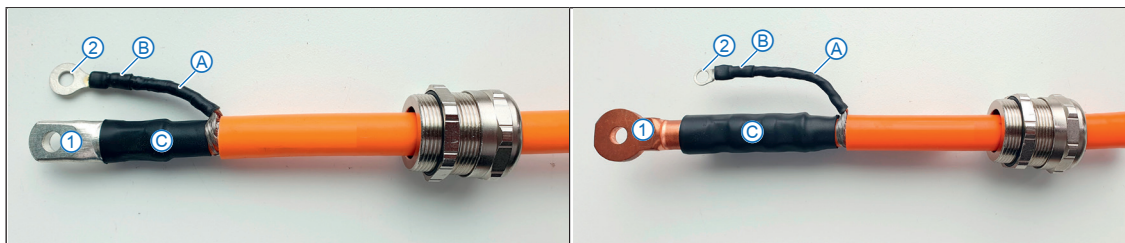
HV-Leitungen (Querschnitt 70 mm²), links Kupfer und rechts Aluminium
